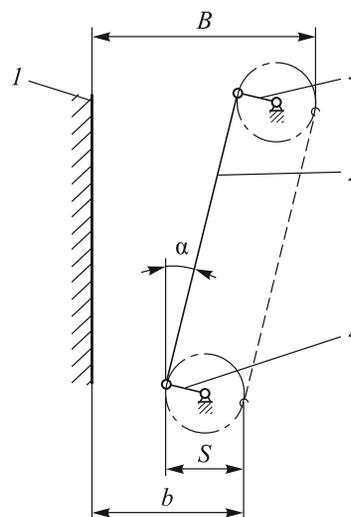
Кинематическая схема дробилки с поступательным движением щеки:
